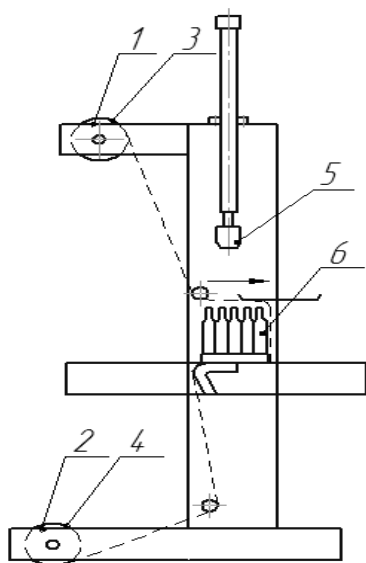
Схема механізму утворення рукава пакувального матеріалу.
